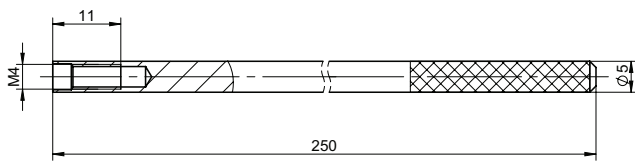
Ausziehwerkzeug Typ 1319 für Blindsensor Typ 6442
